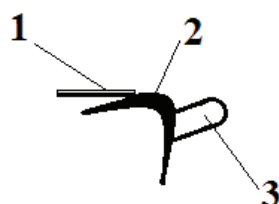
Конструкция боковой присоски: 1 – зеркало; 2 – корпус; 3 – резиновый баллончик
